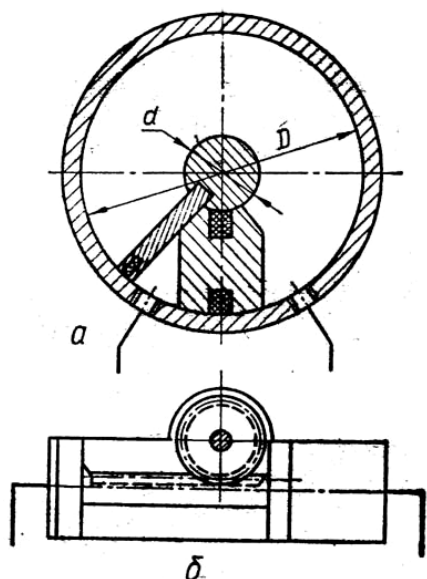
Поворотні пневмодвигуни: а – шибєрний; б – із зубчасто-рейковою передачею
